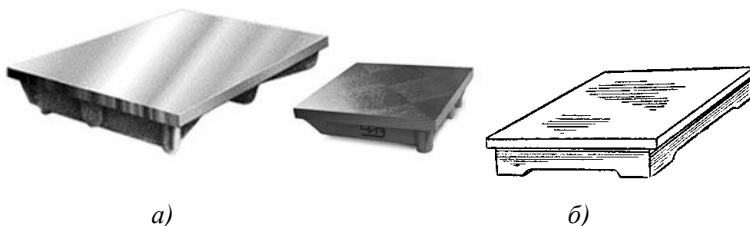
Плиты – поверочные, разметочные (а) и рихтовочные (б) для правки
